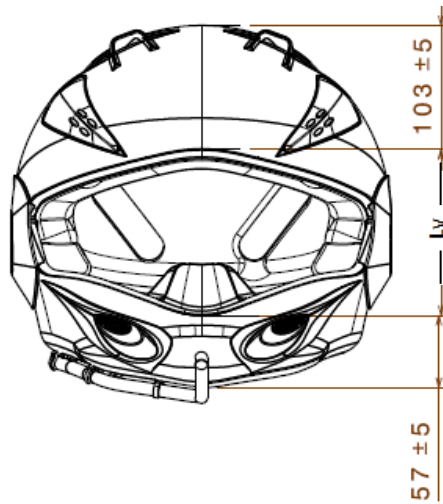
Plano Vista Frontal con Cotas y Tolerancias [Fuente: Elaboración propia]
